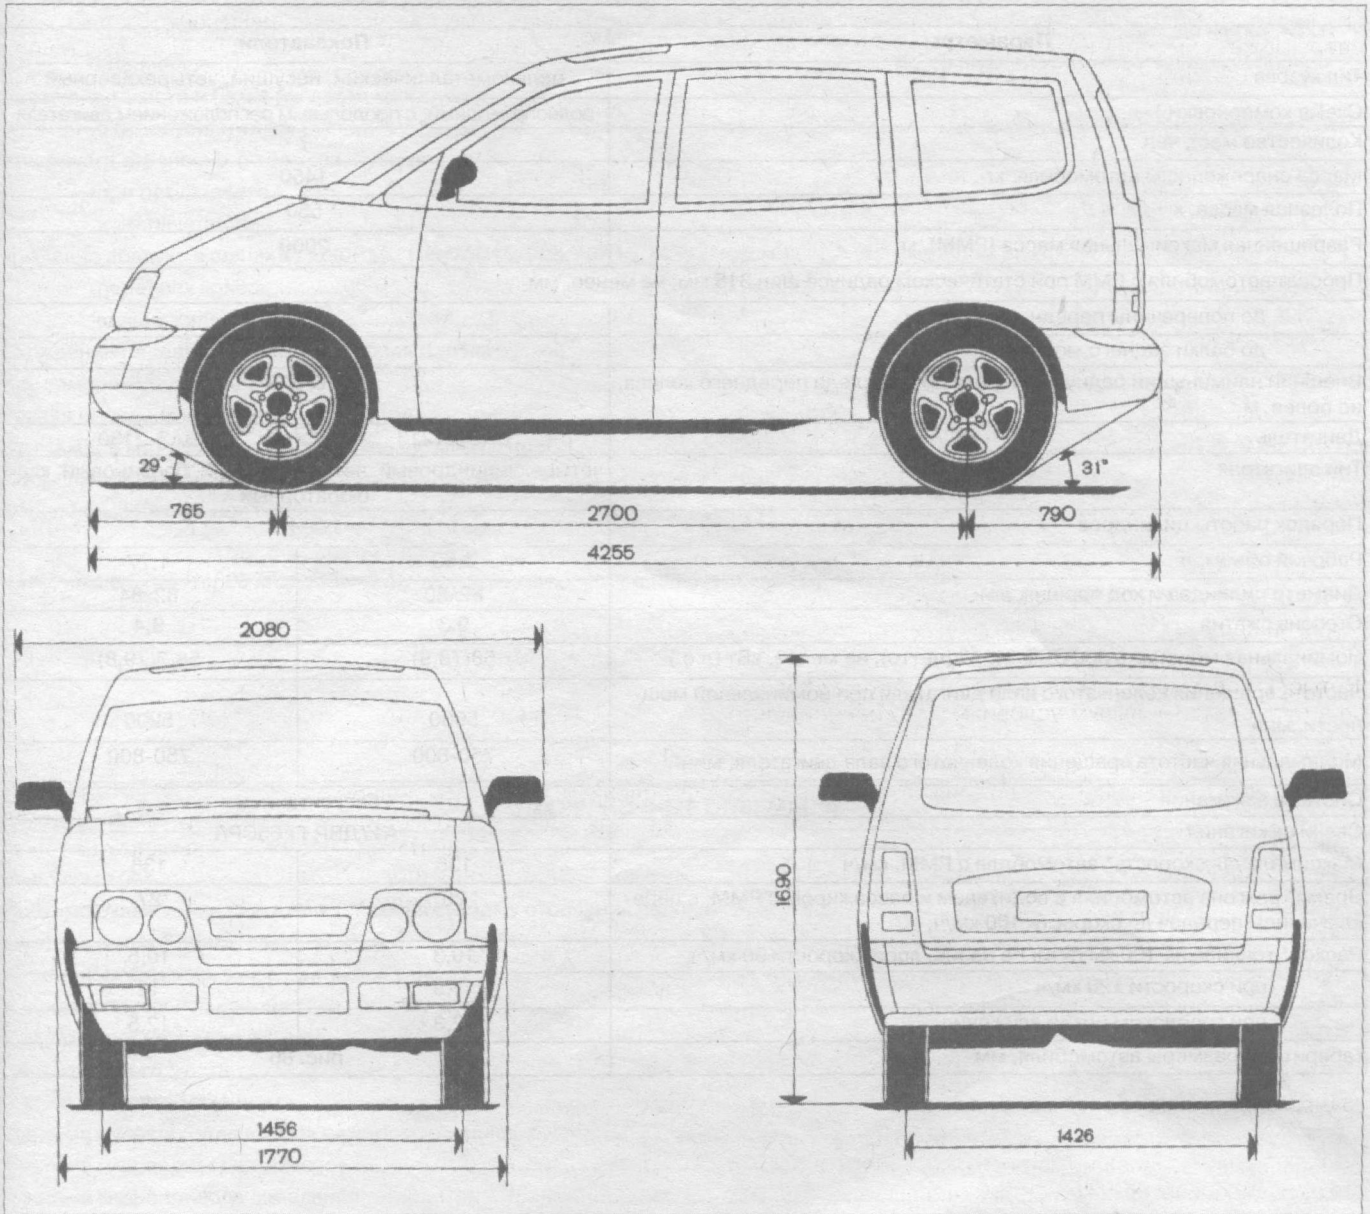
Габаритные размеры автомобиля ВАЗ-2120
